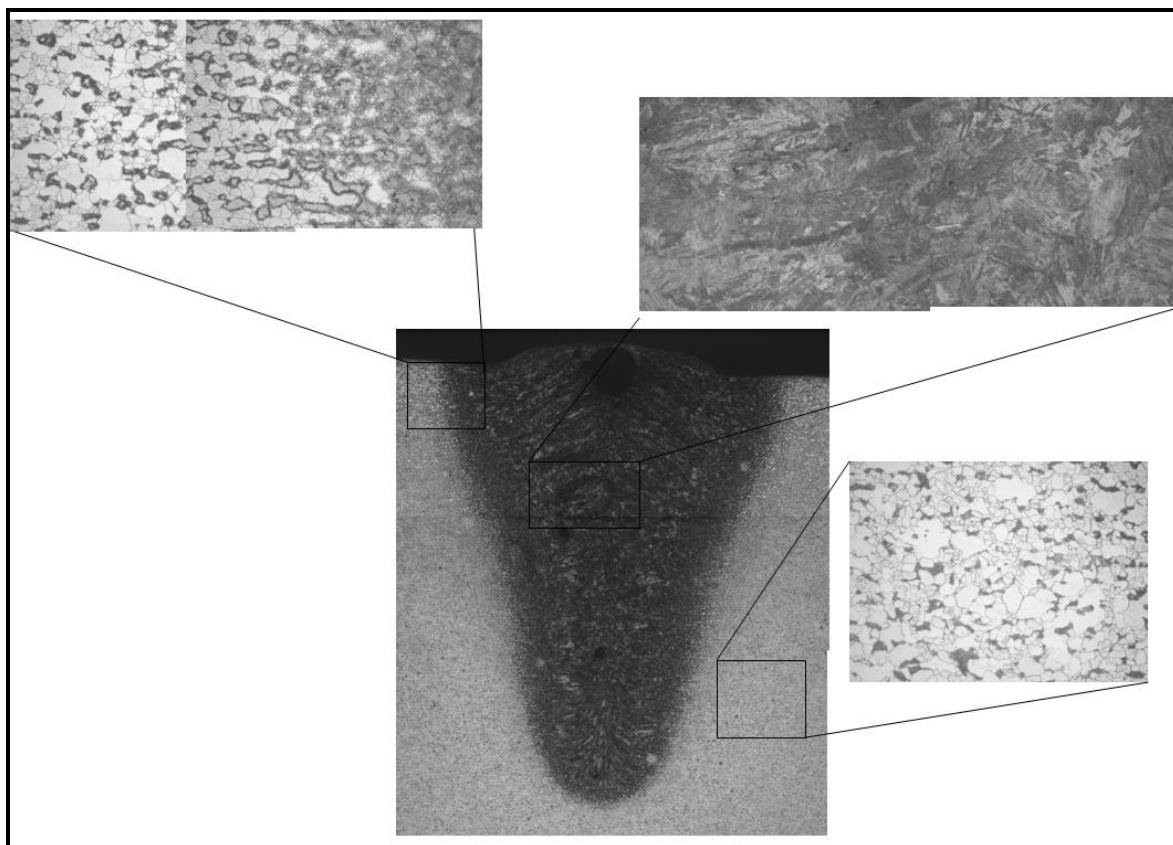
Загальний вид та будова структури зварного з'єднання: сталь 10ХСНД
